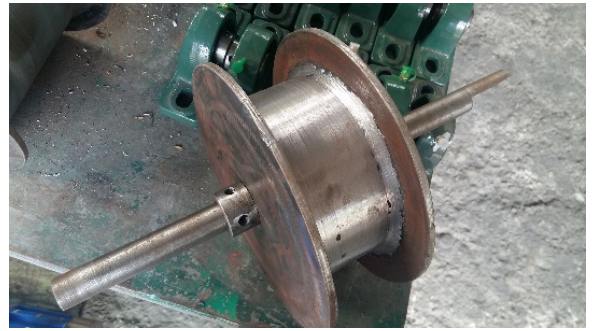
Manufactura de elementos mecánicos. Construcción de carretes para cable de acero.
